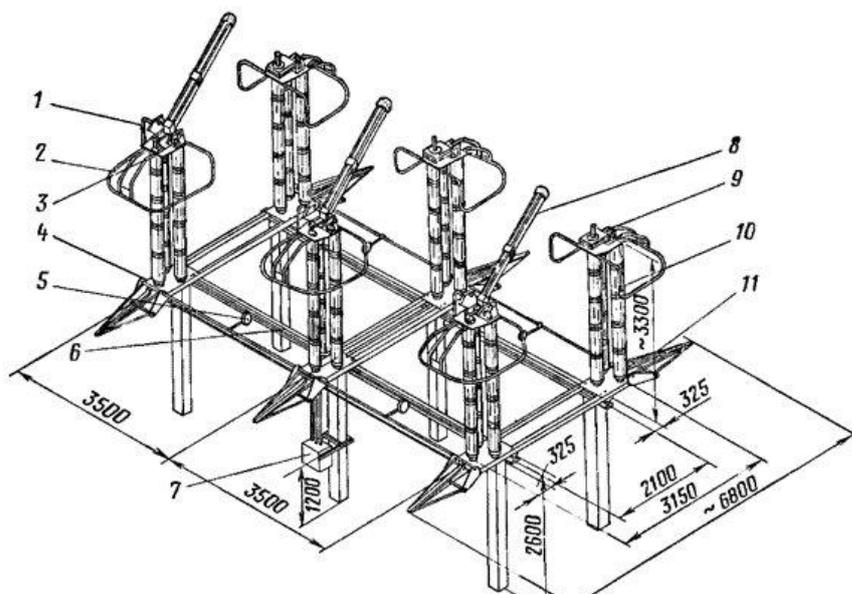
Габаритные размеры разъединителя РНДЗ 220-1000
